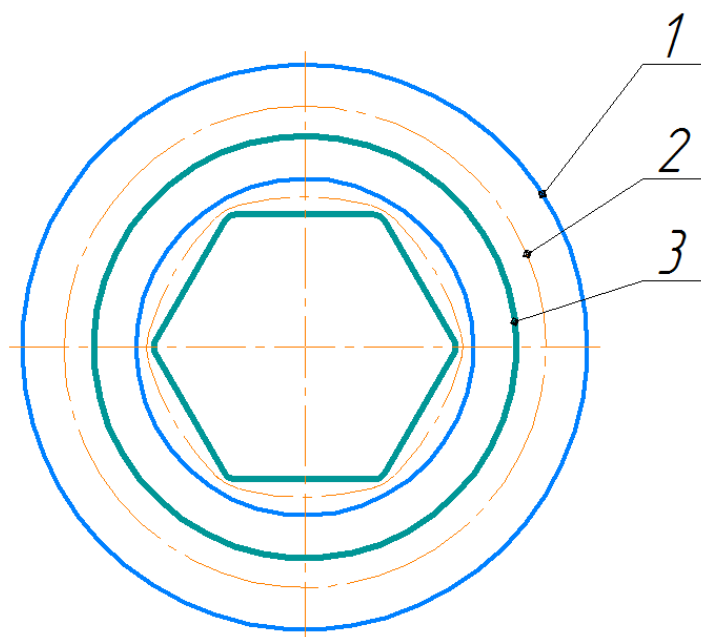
Двухпроходное волочение: круг – внутренний шестигранник. 1- контуры заготовки, 2 - контур промежуточного перехода, 3 - готовая труба.
